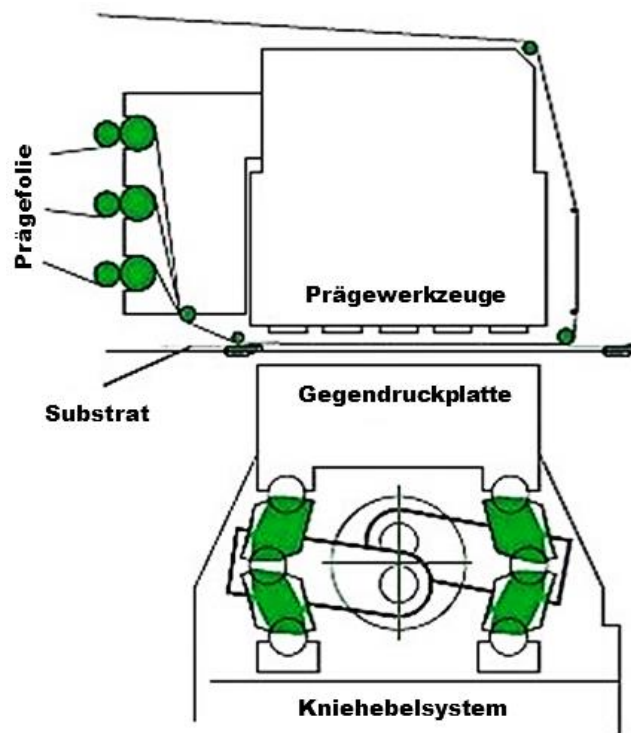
Skizze einer Prägefoliendruckmaschine „Flach auf Flach“. Sowohl das Prägewerkzeug als auch die Gegendruckplatte sind flach. Die Gegendruckplatte wird durch das Kniehebelsystem in Bewegung gebracht. Bildquelle: [ARB05].
